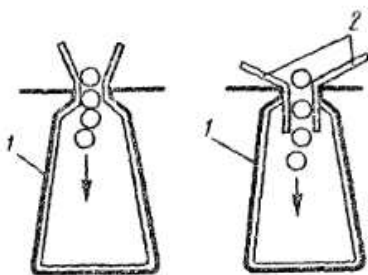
Пазовый короб и вкладыши для укладки обмотки
